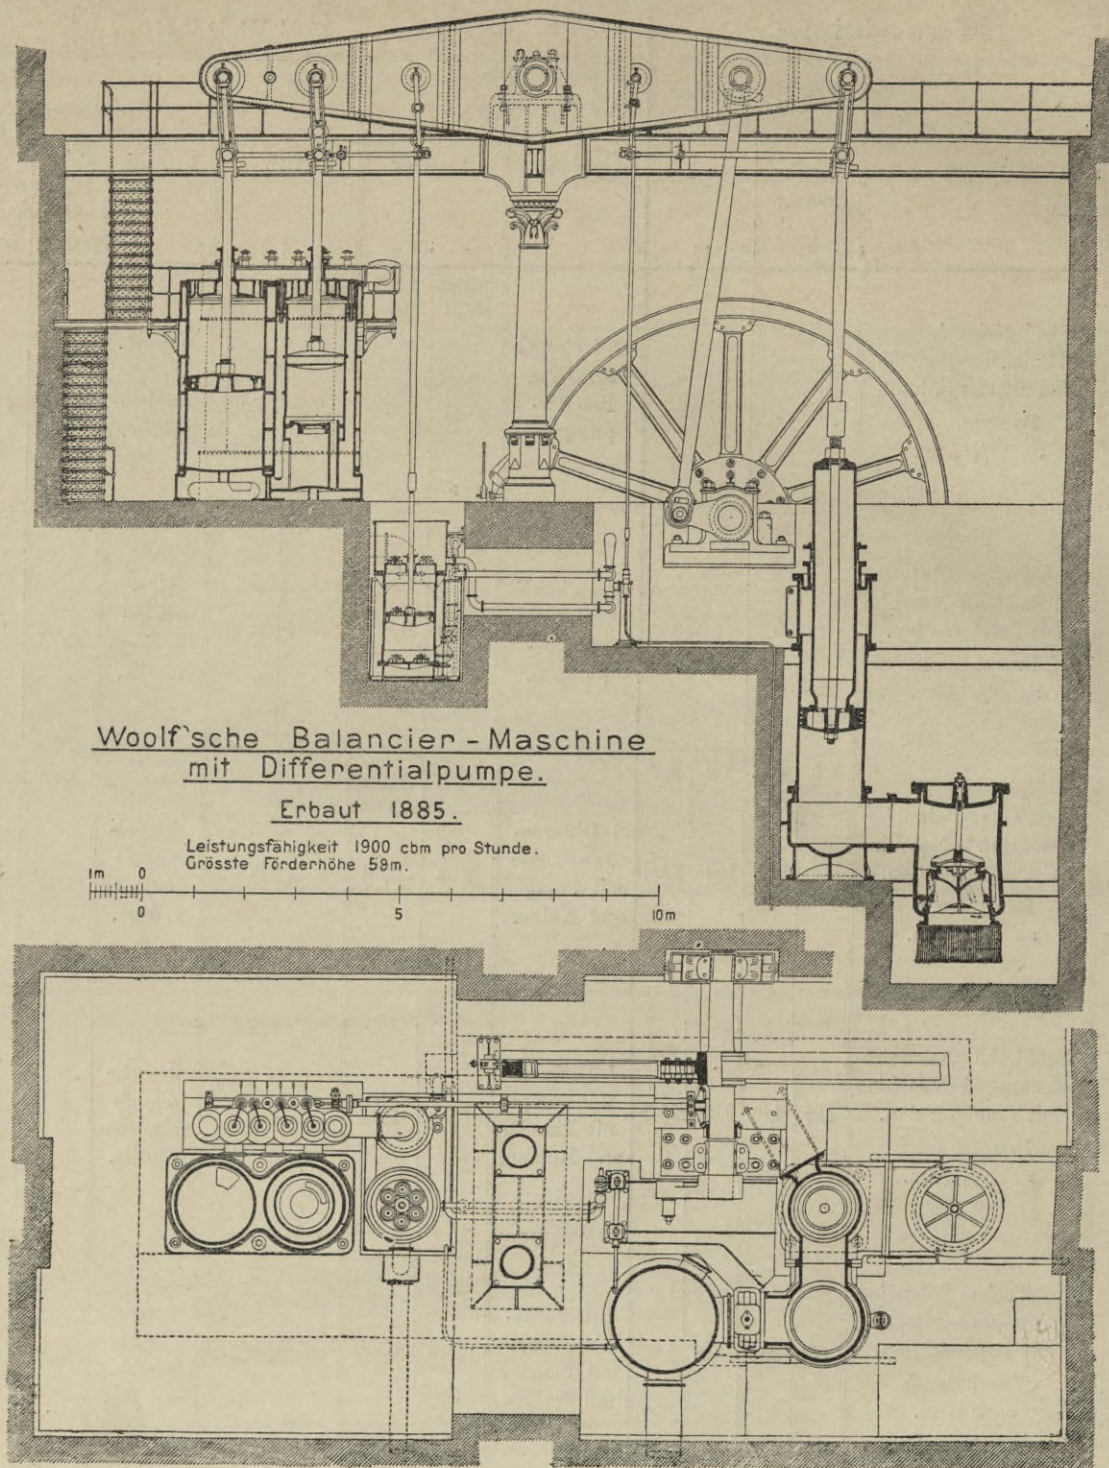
Maschine VII des Pumpwerks Rothenburgsort.
